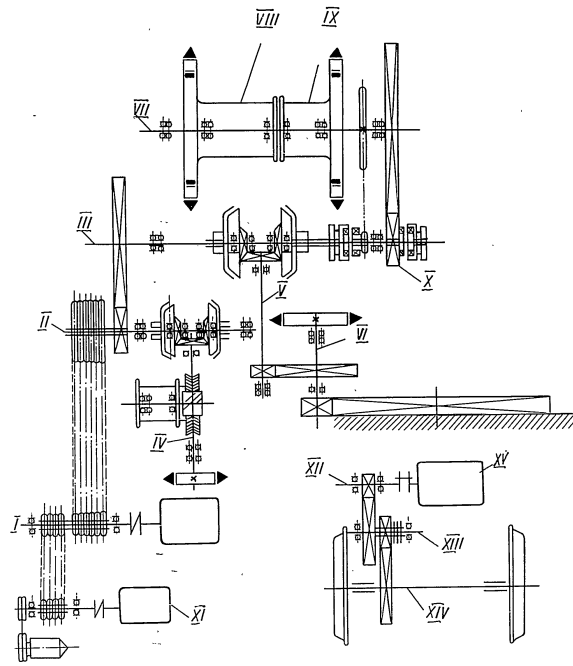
Кинематическая схема крана К-251: I - вал двигателя дизельного; II - трансмиссионный вал; III - промежуточный вал; IV - вал червячной передачи; V - вал реверса поворотного механизма; VI - вал поворотного механизма; VII - вал главной лебедки; VIII - барабан главного подъема; IX - барабан вспомогательного подъема; X - реверс главной лебедки; XI - генератор; XII - вал электродвигателя ходовой тележки; XIII - редуктор; XIV - приводной вал; XV - электродвигатель тележки
